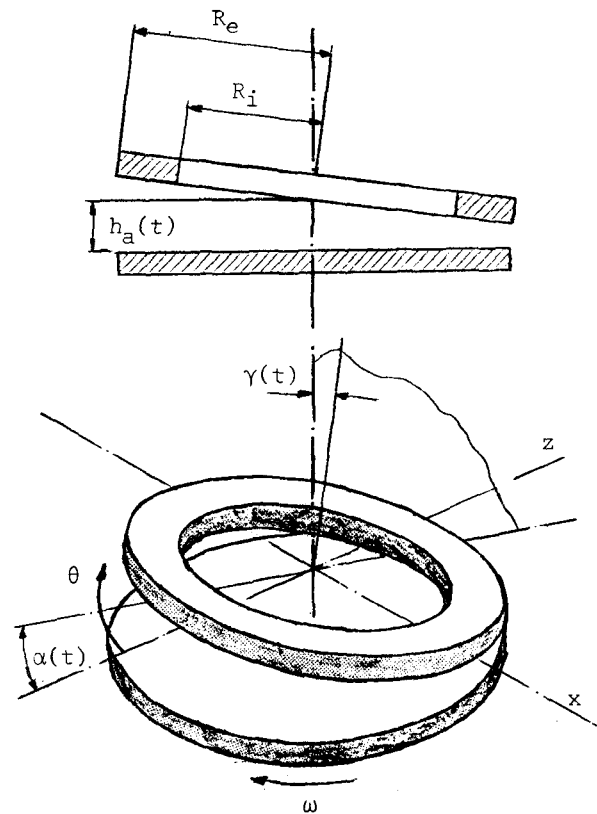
Geometría del retén y sistema de coordenadas utilizado.
